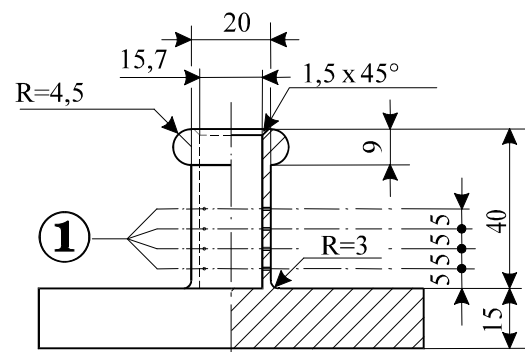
Hohler Bronzeyylinder, einseitig verschlossen.
